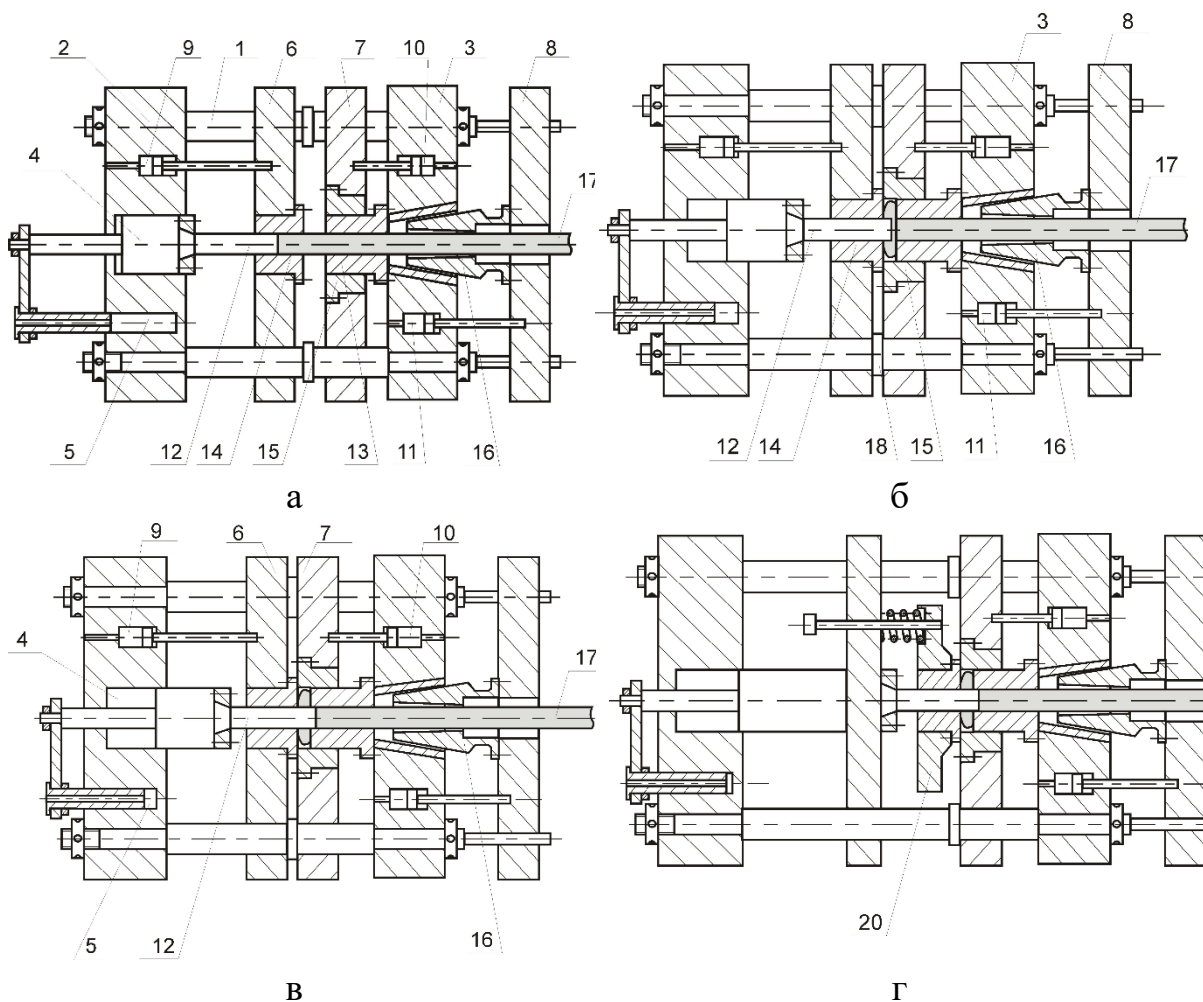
Схема работы гидроустановки для комбинированного выдавливания – пробивки деталей типа колец
